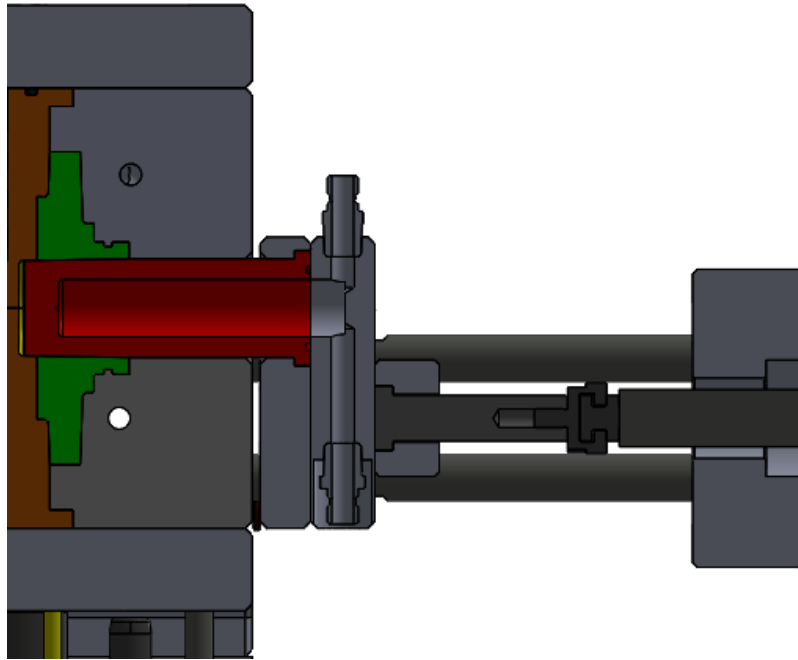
Sistema de Moldeo con Actuador, Molde Cerrado
